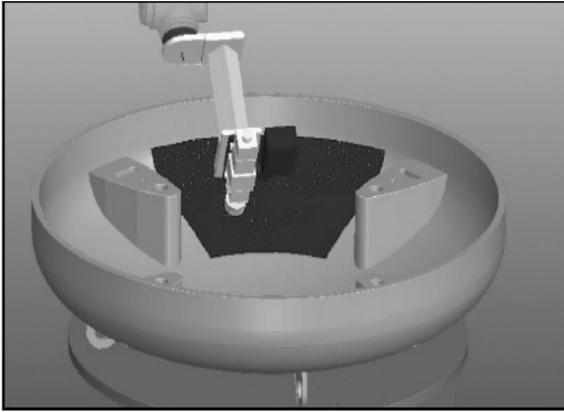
SAW(Submerged Arc Welding)을 이용한 원자로 셀 내부 클래딩
